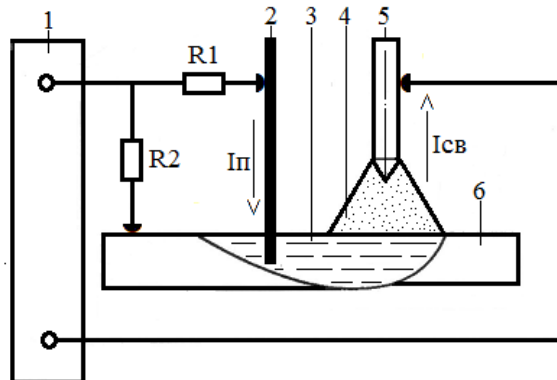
Схема проведения экспериментов: 1 – источник питания; 2 – присадочная проволока; 3 – сварочная ванна; 4 – сварочная дуга; 5 – вольфрамовый электрод; 6 – свариваемый образец.
